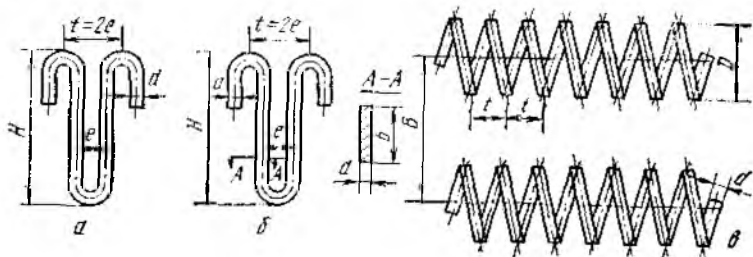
Проволочный зигзагообразный (а); ленточный зигзагообразный (б); и спиральный (в) нагреватели
